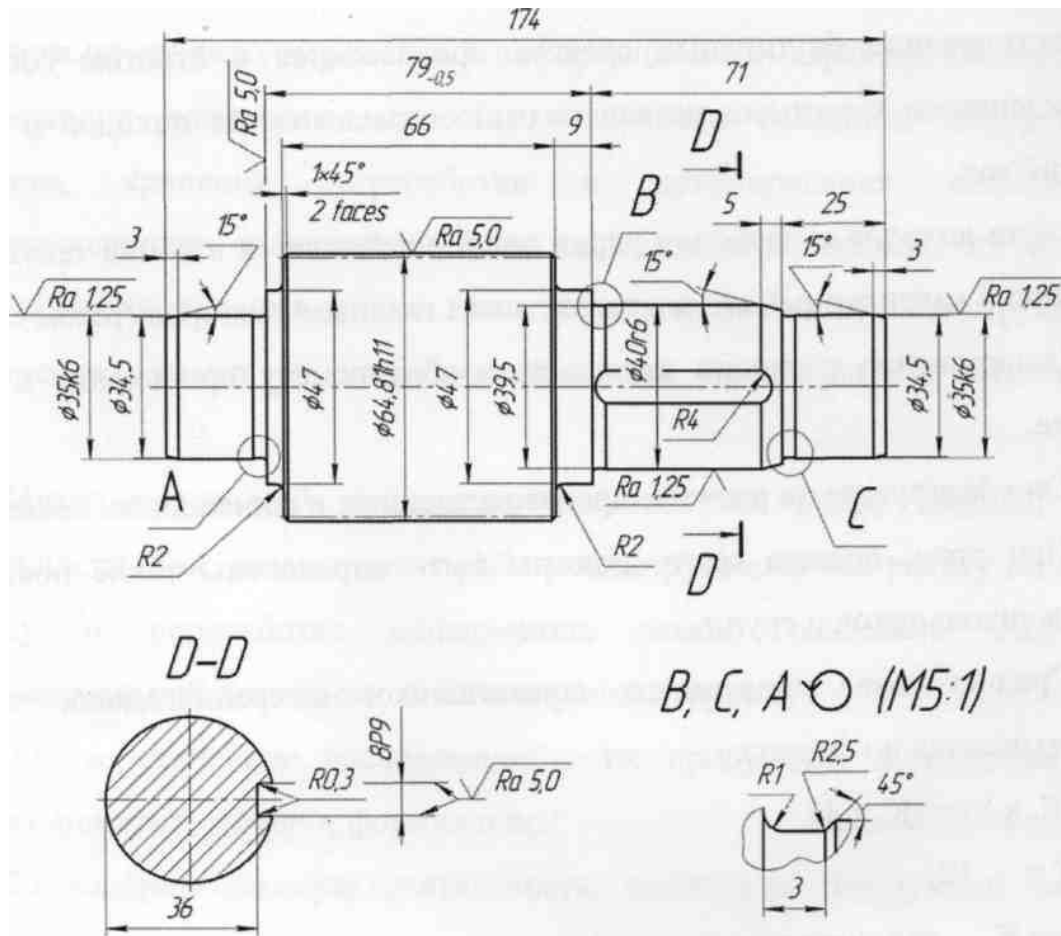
Чертёж вала-шестерни редуктора
